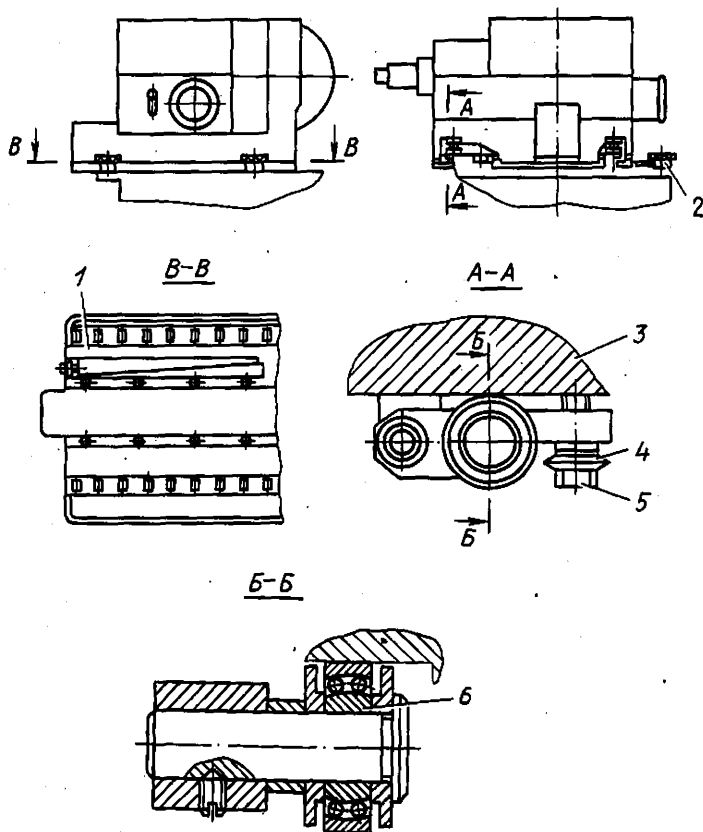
Регулировка и контроль предварительного натяга в направляющих шлифовальной бабки
